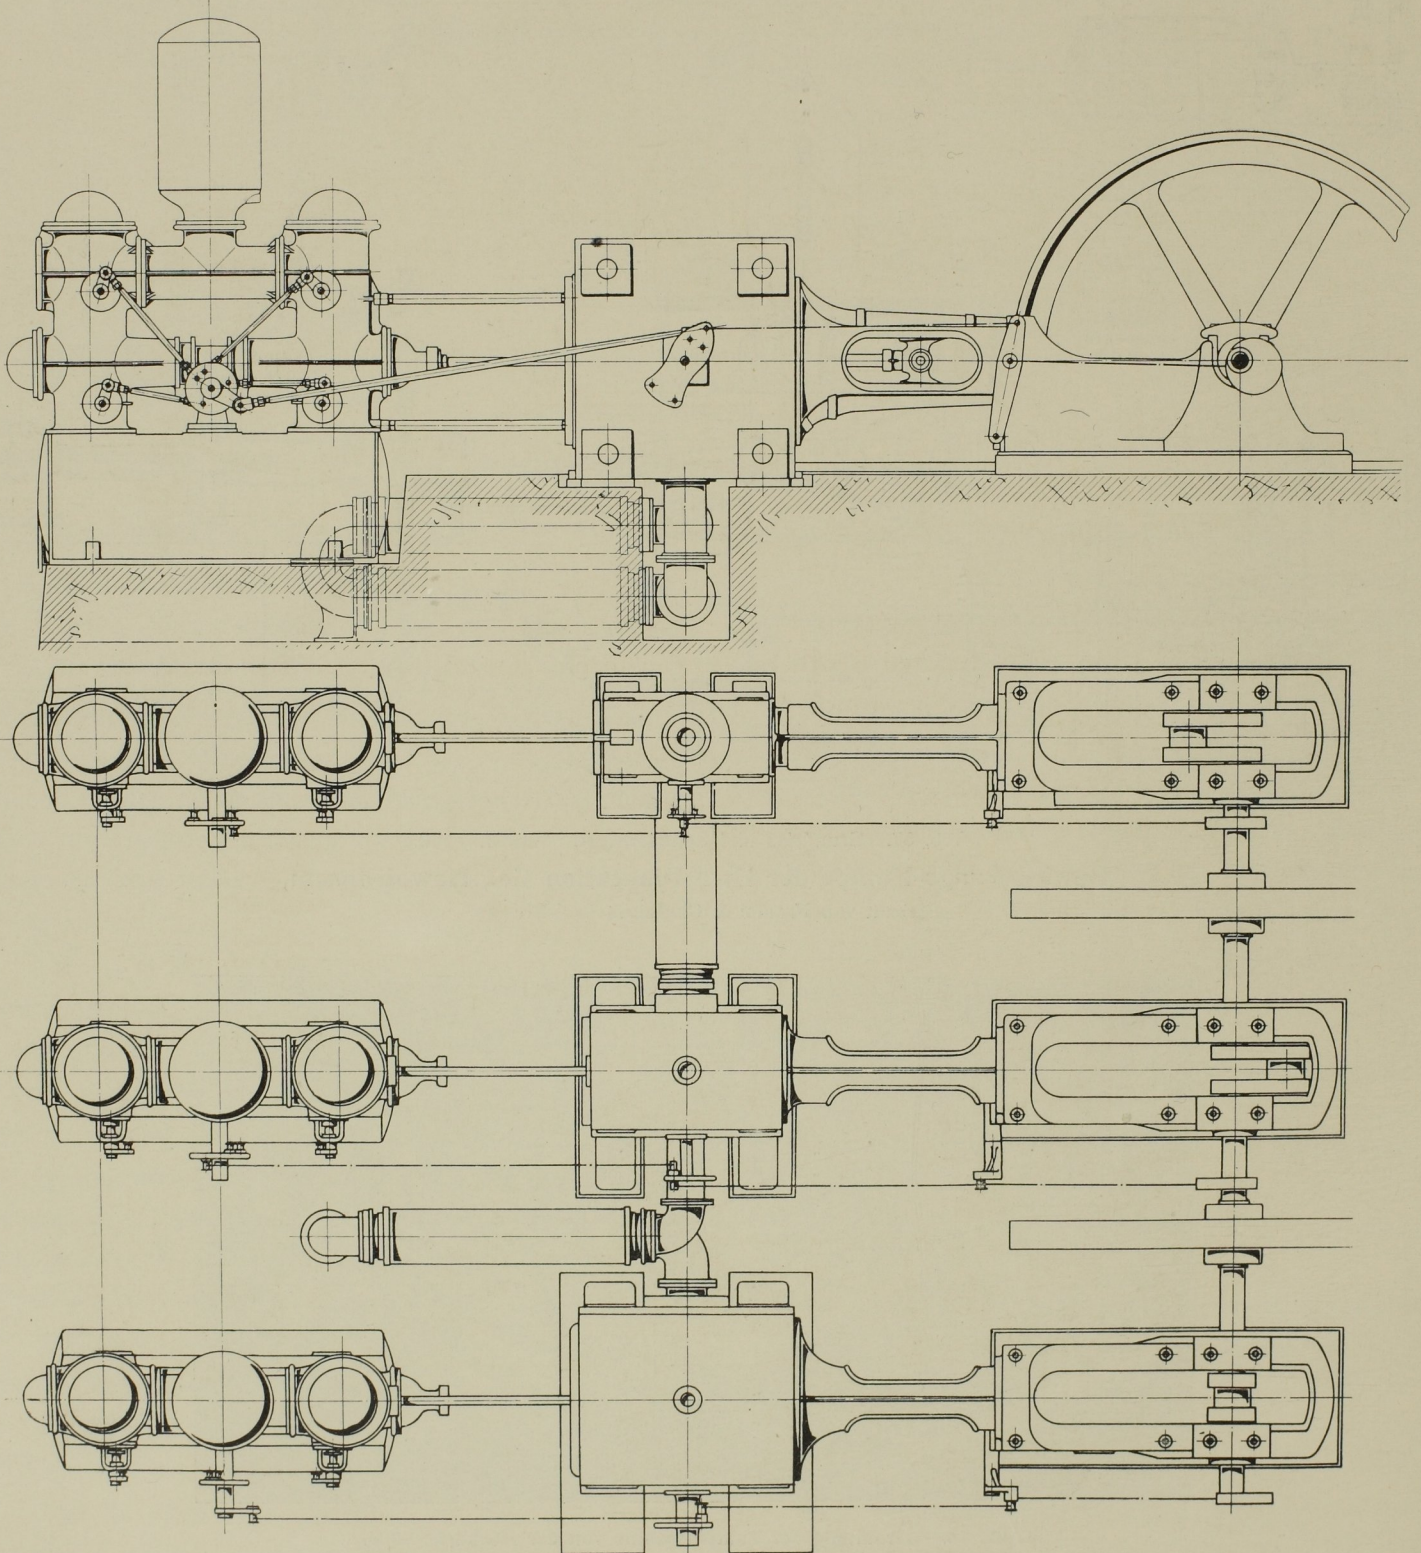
Seitenansicht und Grundriss der Pumpmaschine.
